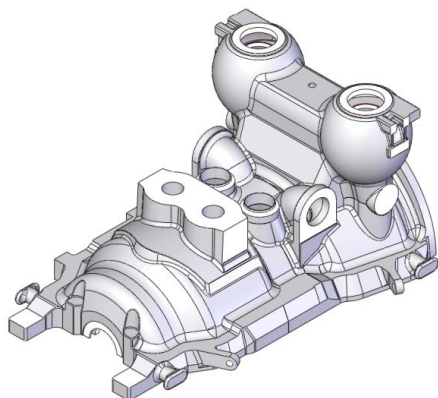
Отливка «верхняя часть корпуса паровой турбины».
